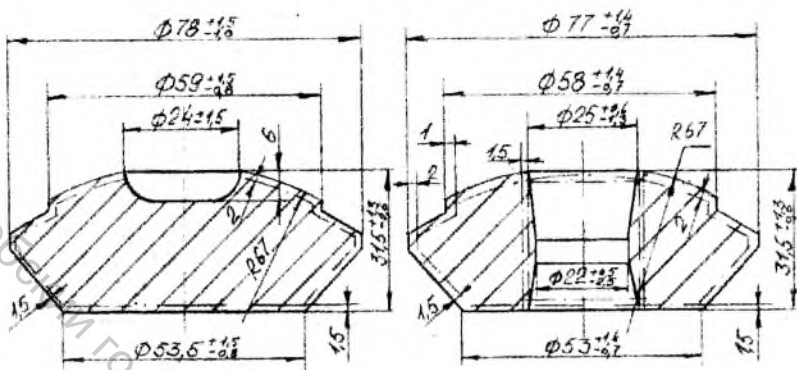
Чертежи поковок дифференциала автомобиля
